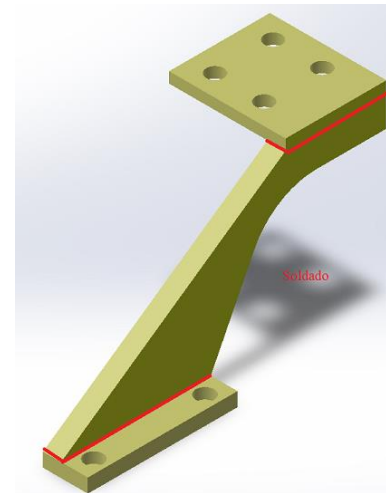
Vista de montaje de pieza N°5 en la parte superior de la estructura (Fuente 91)
